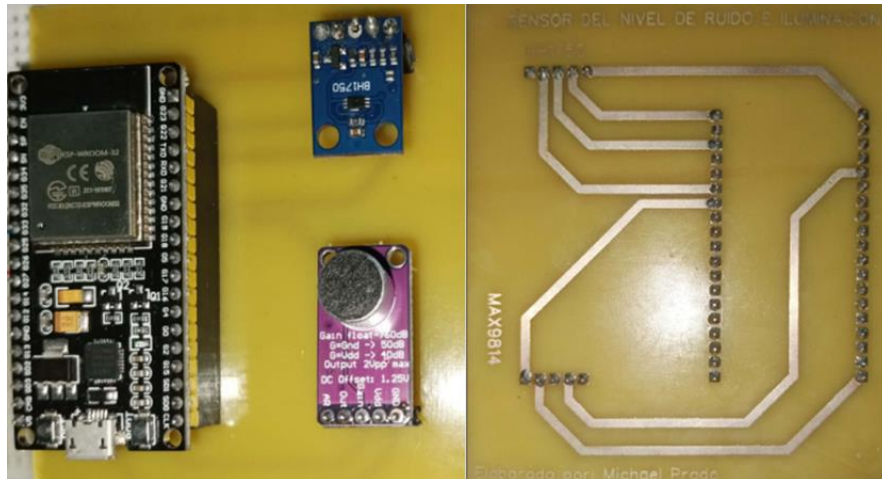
Capa superior e inferior de placa PCB terminada.
